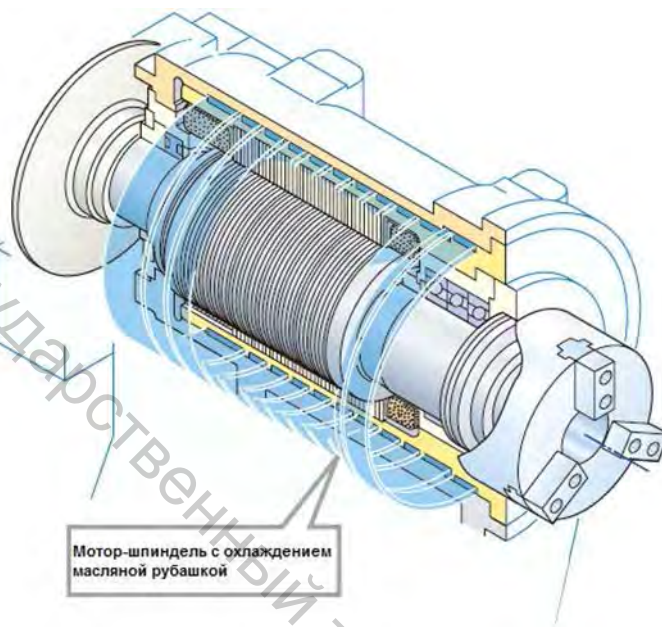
Общий вид мотор-шпинделя токарного станка с ЧПУ
